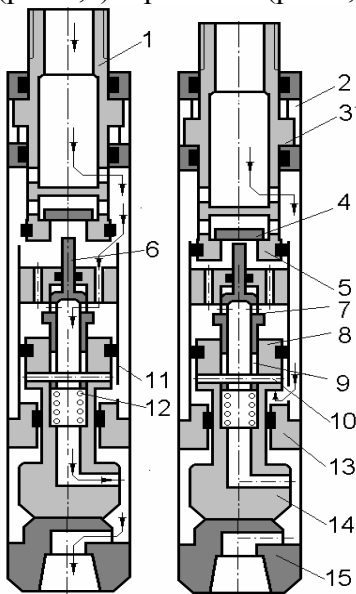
Схема гидроударника: 1 – шток; 2 – шлицевой переходник; 3 – шлицы штока; 4 – впускной клапан; 5 – седло; 6 – толкатель; 7 – упор; 8 – поршень; 9 – паз; 10 – палец; 11 – цилиндр; 12 – пружина; 13 – верхняя наковальня; 14 – боек; 15 – нижняя наковальня
